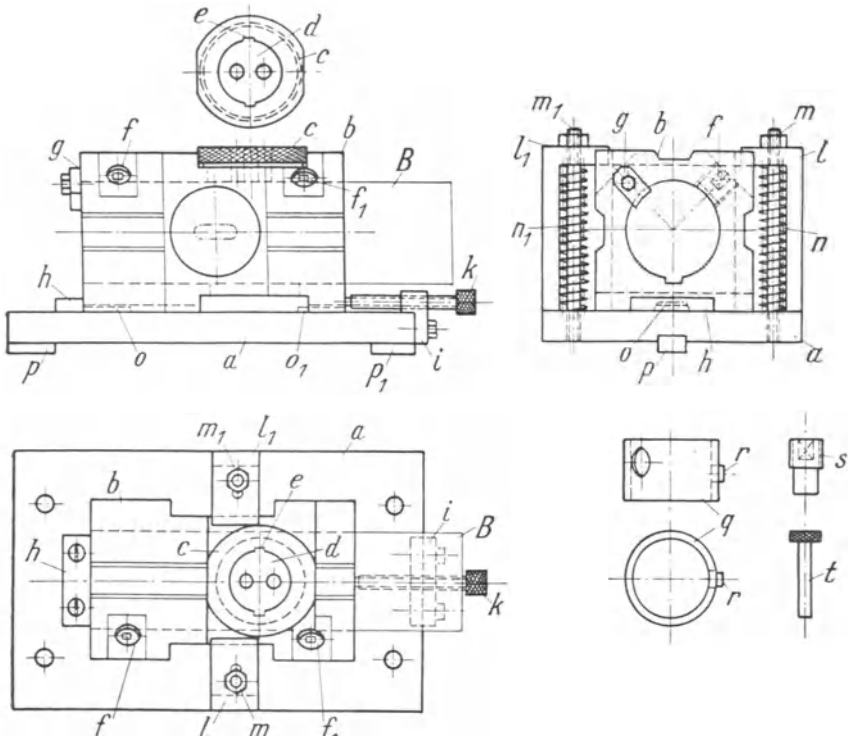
Vorrichtung zum Bohren und Fräsen der Schlitze in Bohrstäben und Hülsen.
